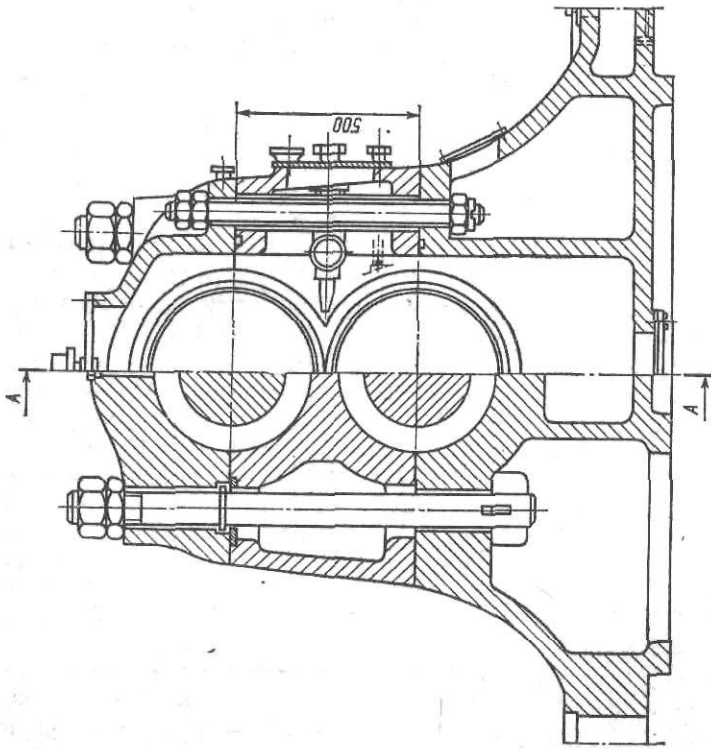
Шестеренная клетка для привода валков среднесортного стана 350 конструкции Э3ТМ
